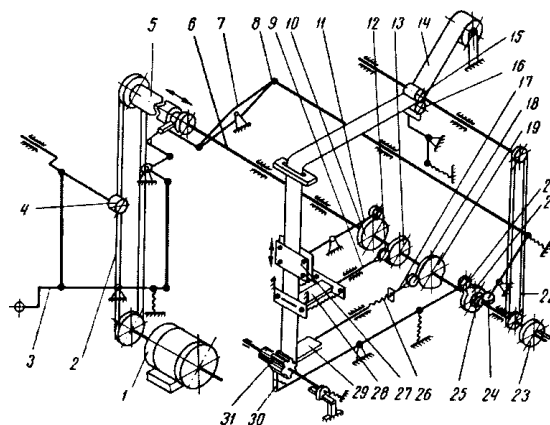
Кинематическая схема станка для изолировки пазов якоря.
